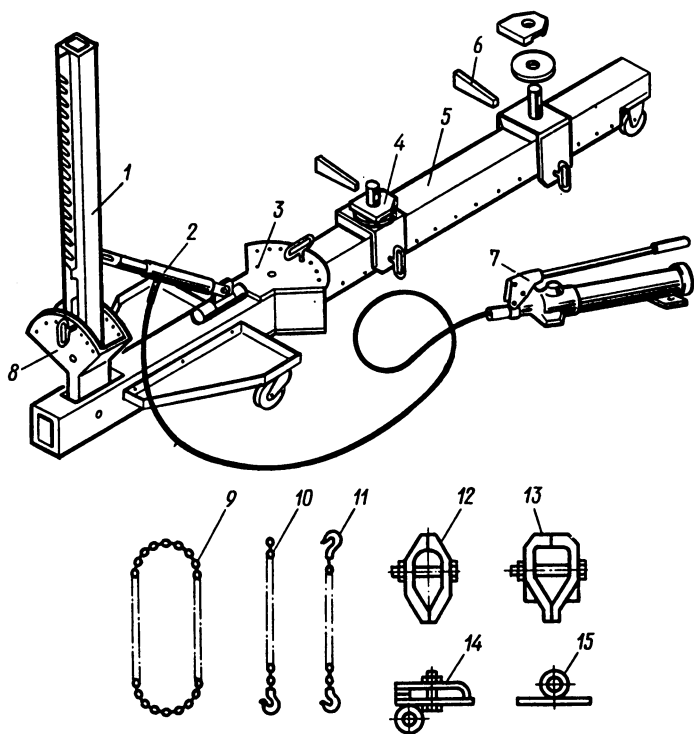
Общий вид устройства для правки кузовов БС-124.000
